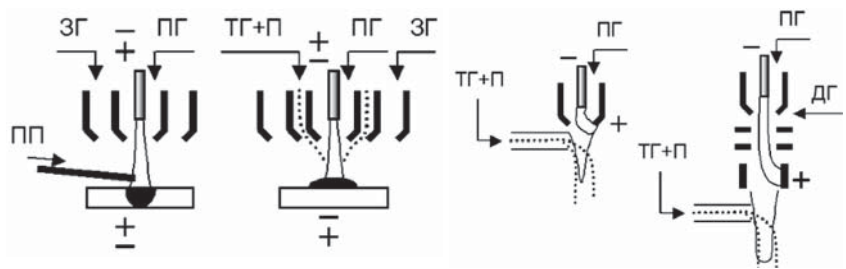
Схемы плазмотронов для сварки (а), наплавки (а, б), напыления (в, г), финишного плазменного упрочнения (г), микроплазменной обработки (в — без П и ТГ); газы: ПГ — плазмообразующий, ЗГ — защитный, ТГ — транспортирующий, ДГ — дополнительный; ПП — присадочная проволока; П — порошок или реагенты упрочнения.
